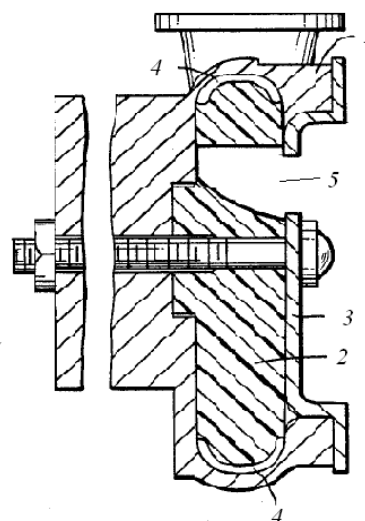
Схема обработки внутренней поверхности центробежного насоса с выравнивающим приспособлением [26]
